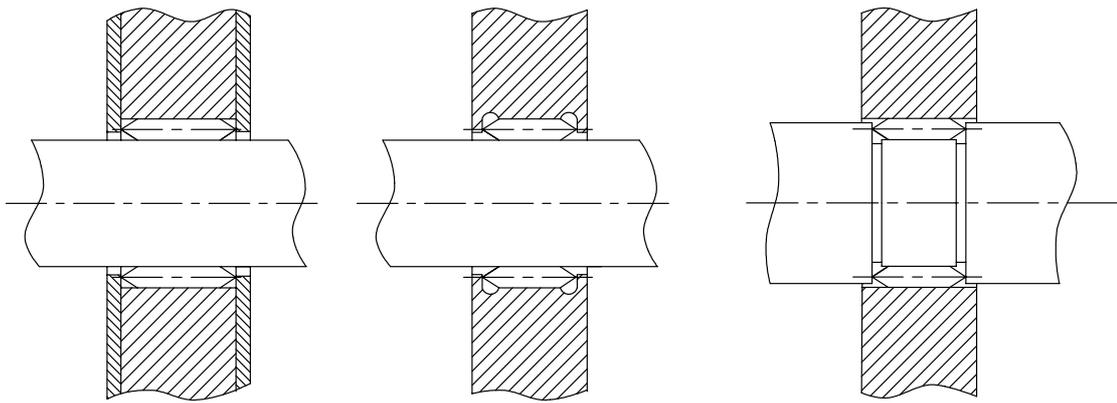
Схемы сборочных единиц с игольчатыми подшипниками
